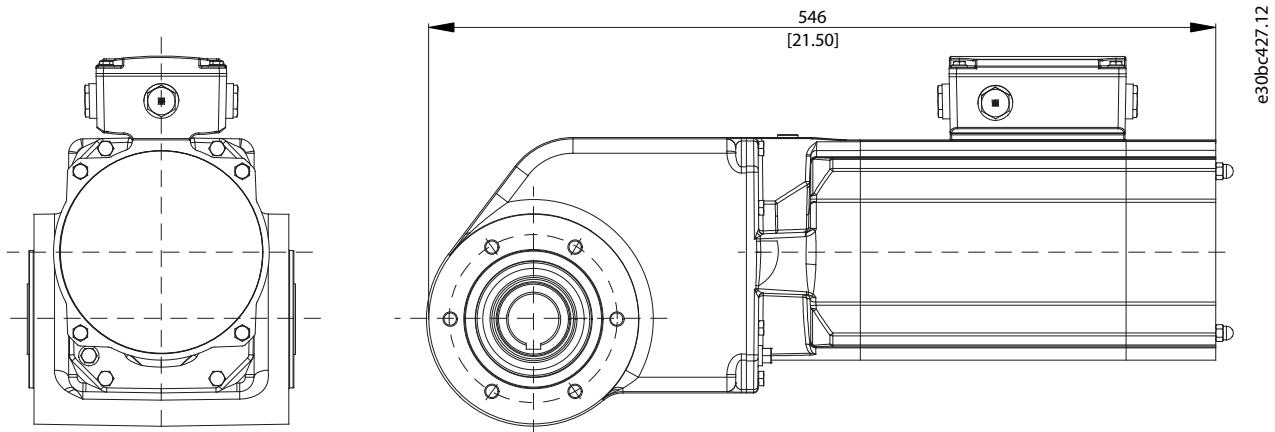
Abmessungen des VLT® OneGearDrive® mit mechanischer Bremsoption
